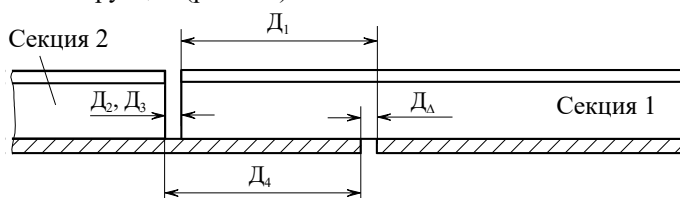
Размерная цепь в стыковом соединении корпусных конструкций:
